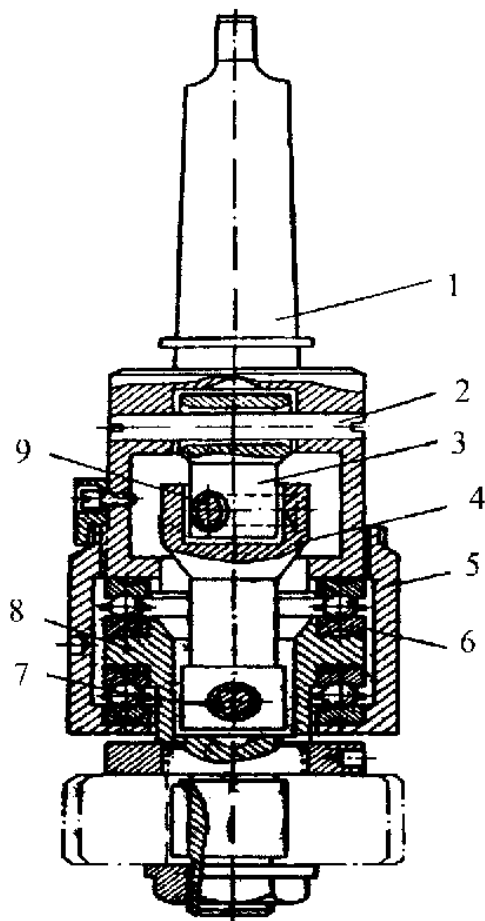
Плаваючий патрон для закріплення розвертки при обробці гільз
